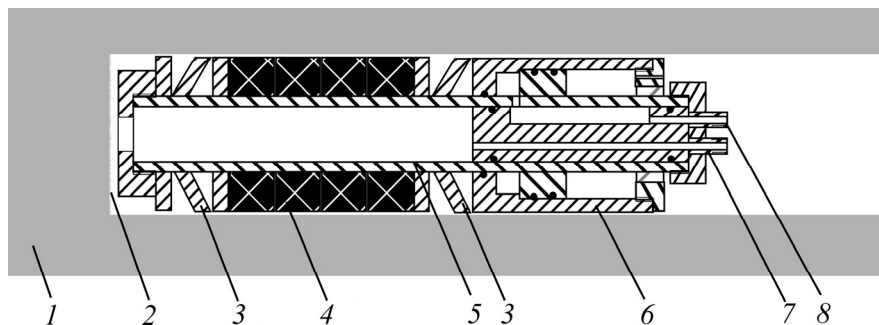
Схема устройства поперечного гидроразрыва УПГ-105 и его размещения в скважине: 1 — породный массив; 2 — забой скважины; 3 — якорь из разрезного пружинного конического кольца толщиной 3 мм; 4 — резиновые уплотнительные элементы толщиной 30 мм (4 шт.); 5 — силовой шток с плунжером; 6 — гидравлический цилиндр; 7 — вход подачи рабочей жидкости в зону разрыва; 8 — вход гидравлического цилиндра
